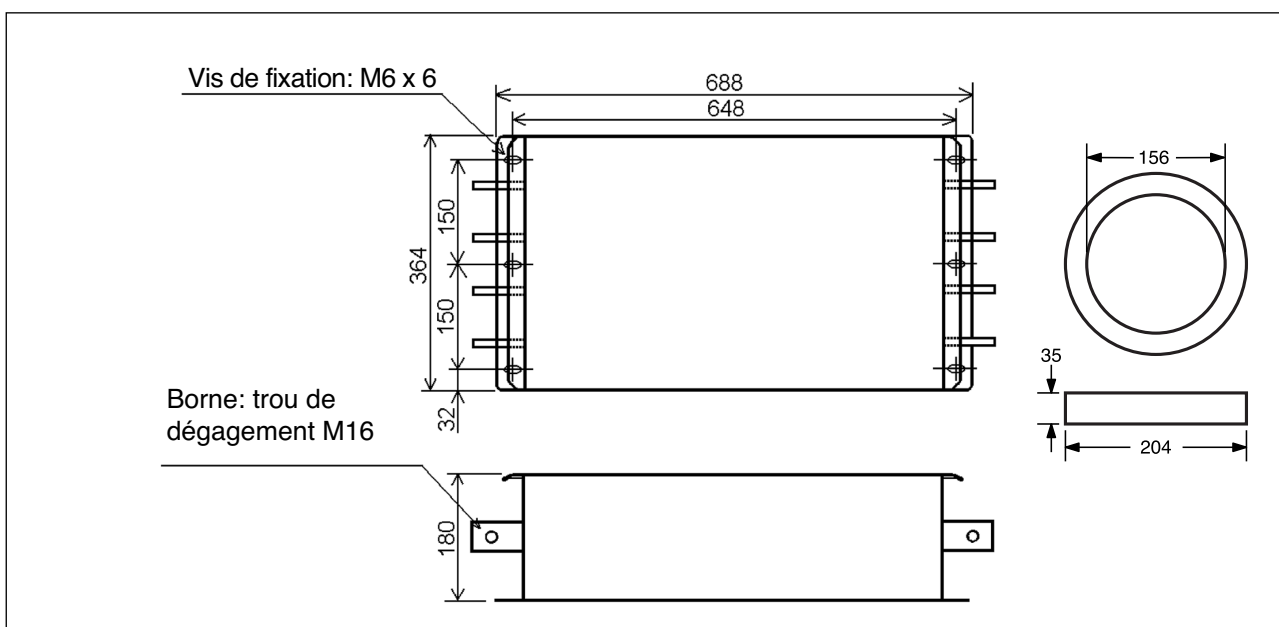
Dimensions externes (RF3880-F11, F200160)
